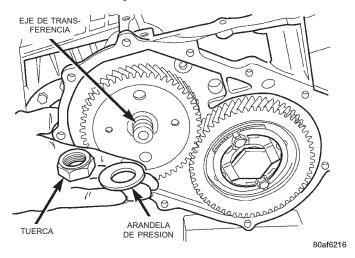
Tuerca del engranaje del eje de transferencia y arandela cónica
